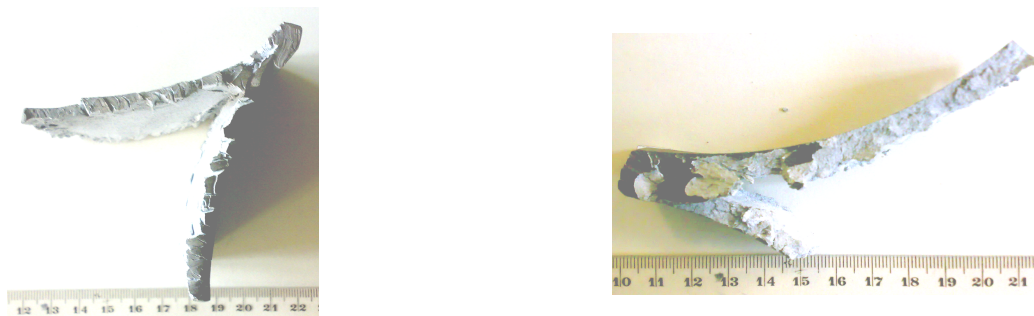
Вид разрушенных образцов в процессе прокатки
